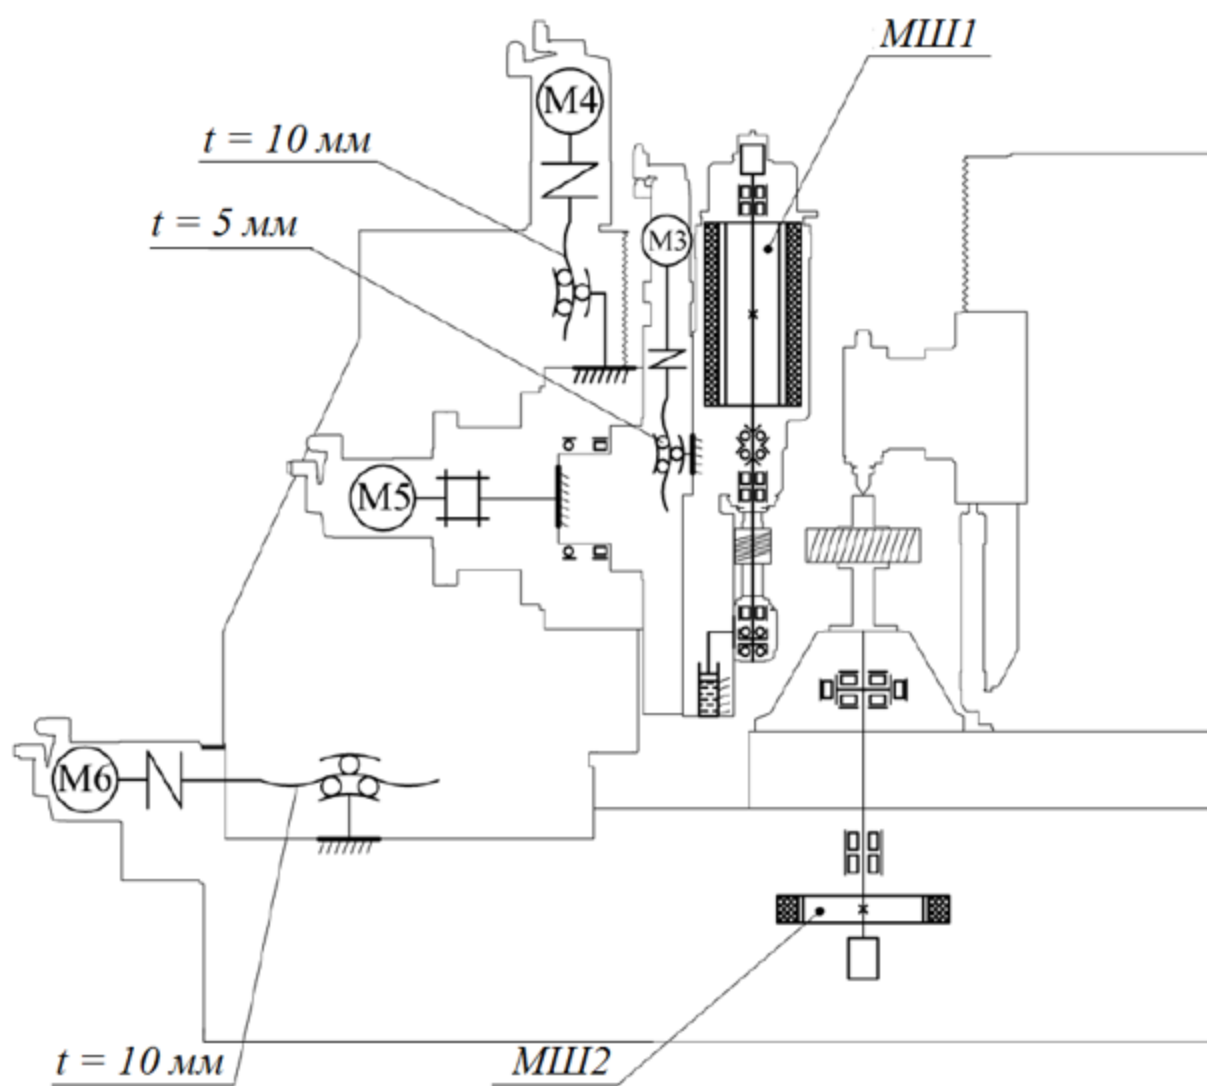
Кінематична схема модернізованого вертикального зубофрезерного верстата
